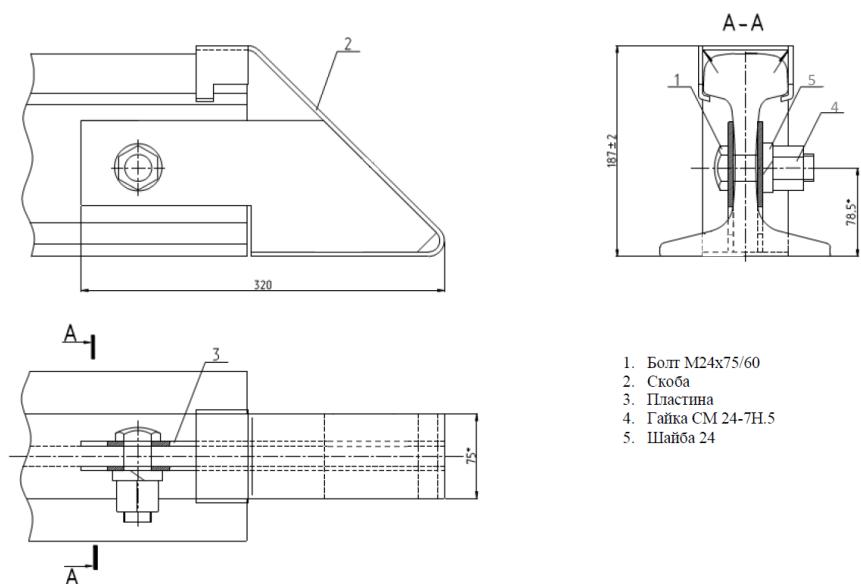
Охранное устройство (башмак) на торцы рельса
